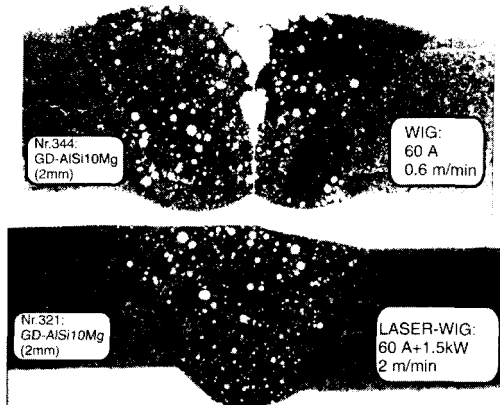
Querschnitte einer WIG- und einer Laserstrahl-WIG-Schweißnaht an 2 mm dicken Al-Druckgußplatten.
